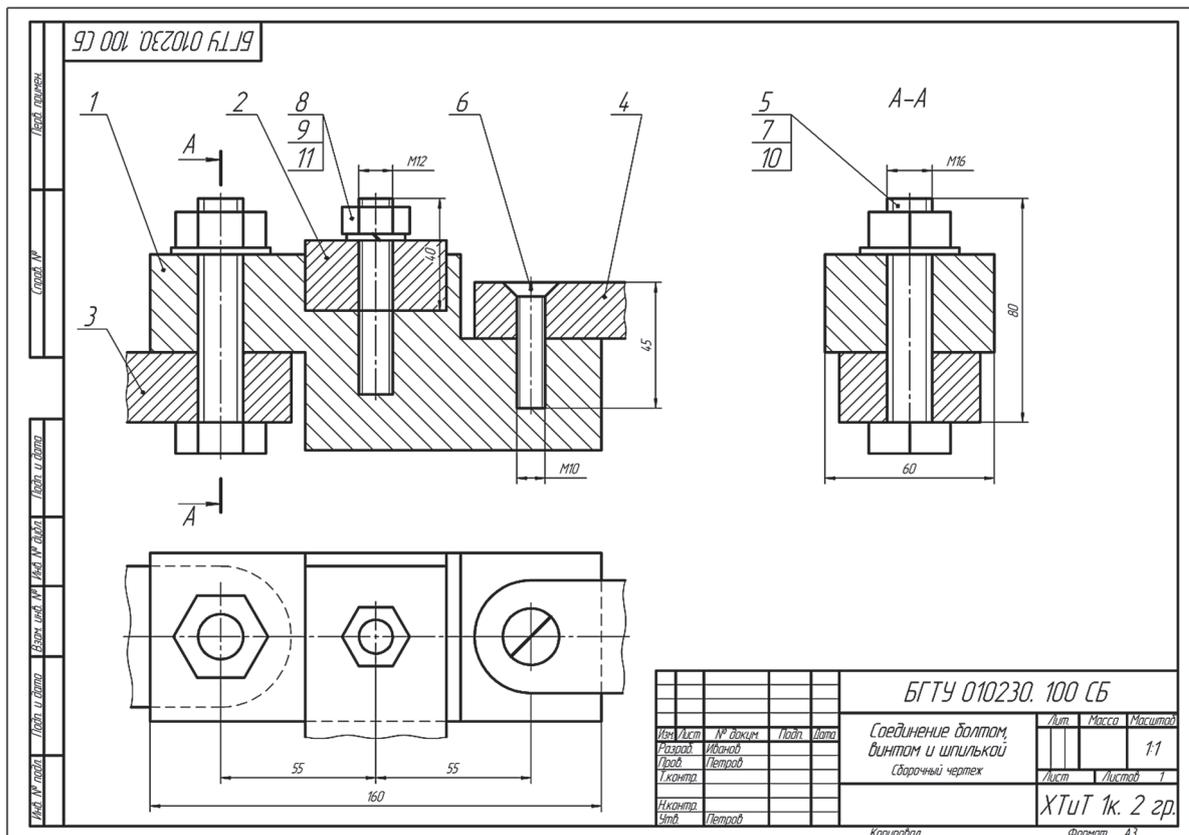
Пример выполнения чертежа соединения болтом, винтом и шпилькой
